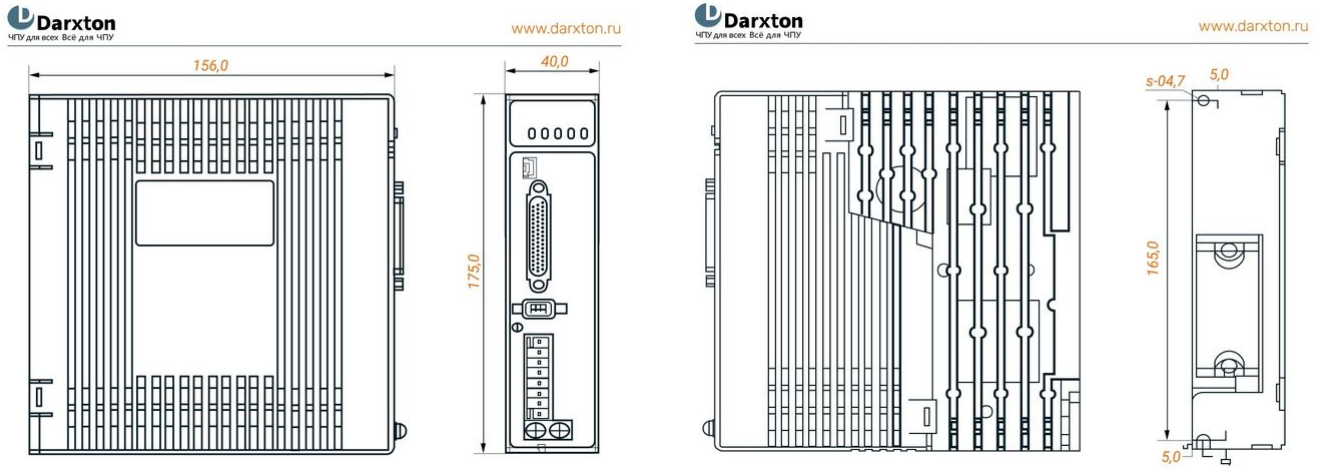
Габаритные размеры драйвера EL7-EC400Z
